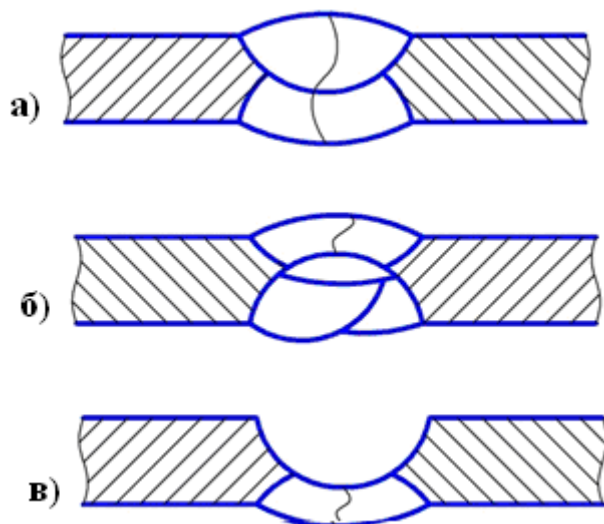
Вариант ремонта трещин сваркой при доступе с одной стороны
